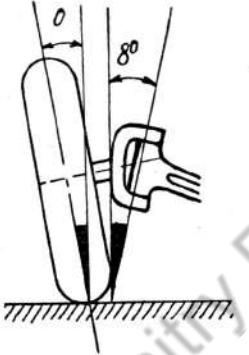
Боковой наклон колеса и шкворня поворотной цапфы
